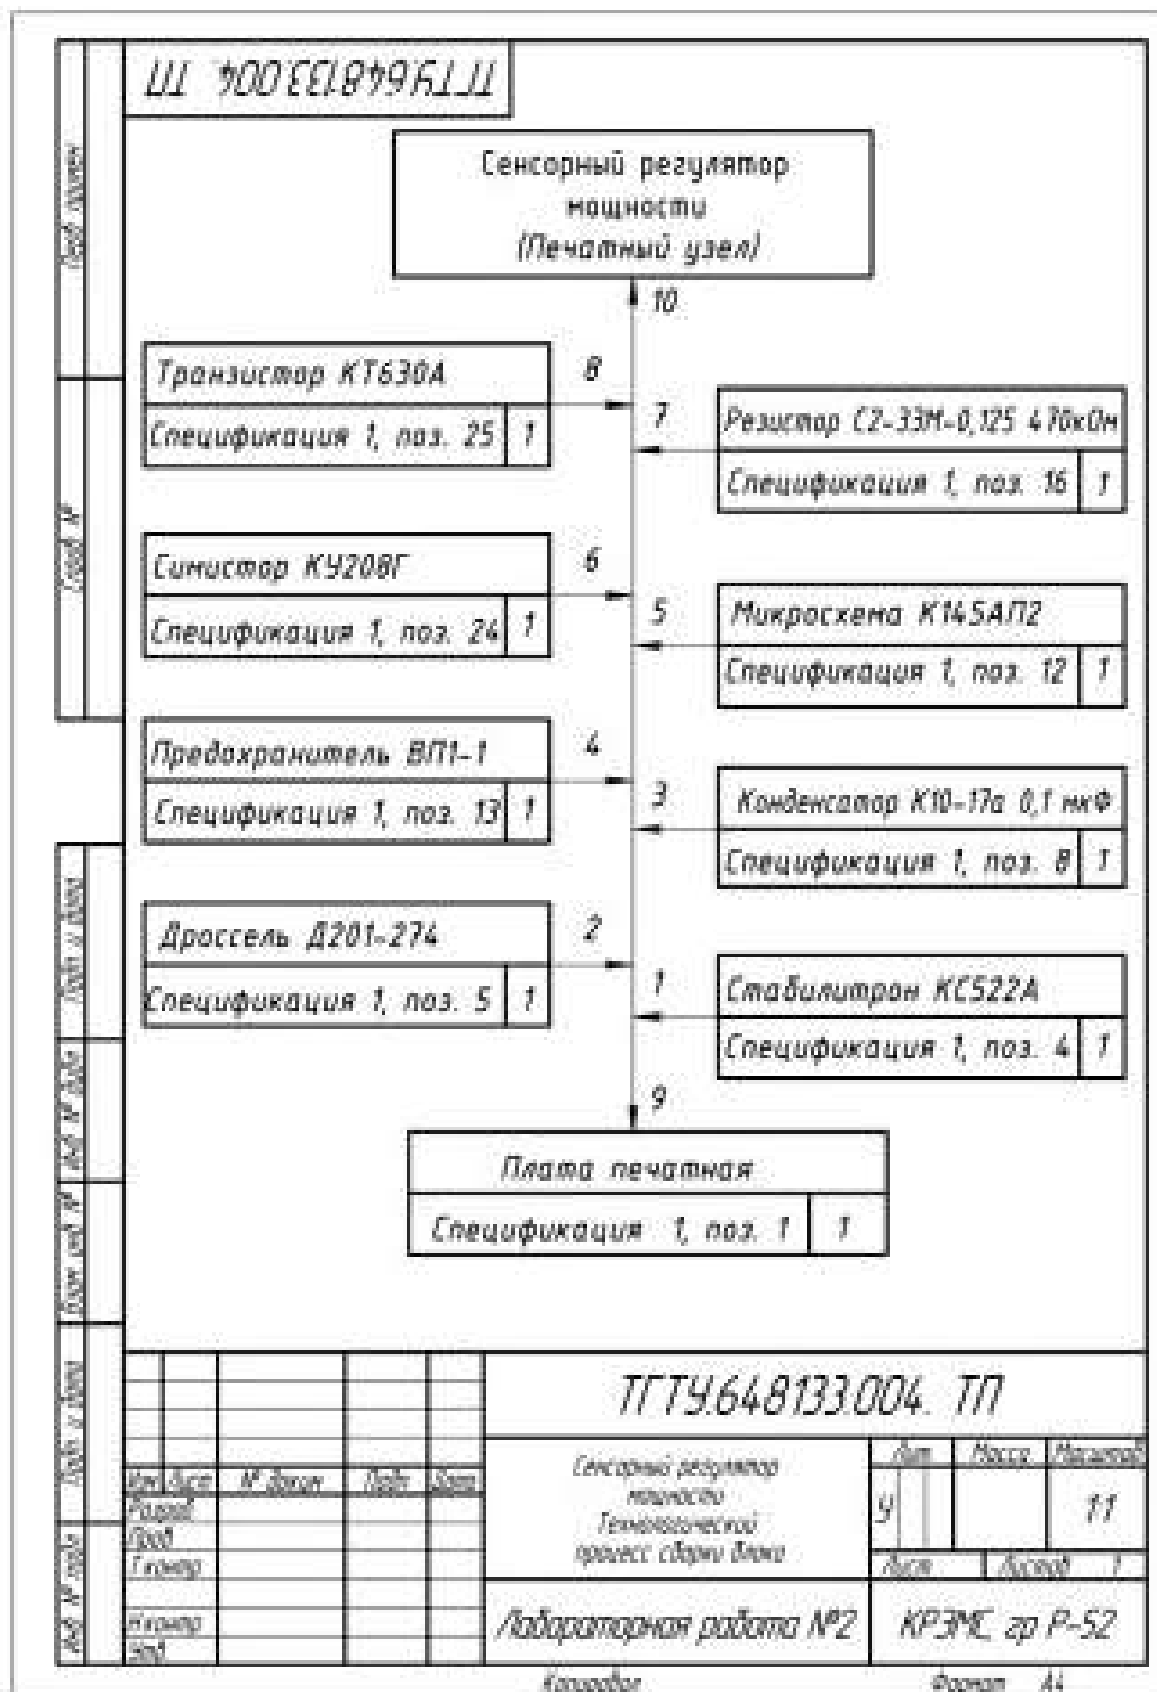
Технологическая схема сборки блока с базовой деталью
